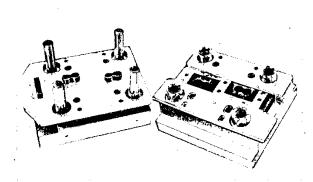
Hartmetallbestücktes Schnittwerkzeug für Kettenlaschen (Widia-Fabrik, Essen)
